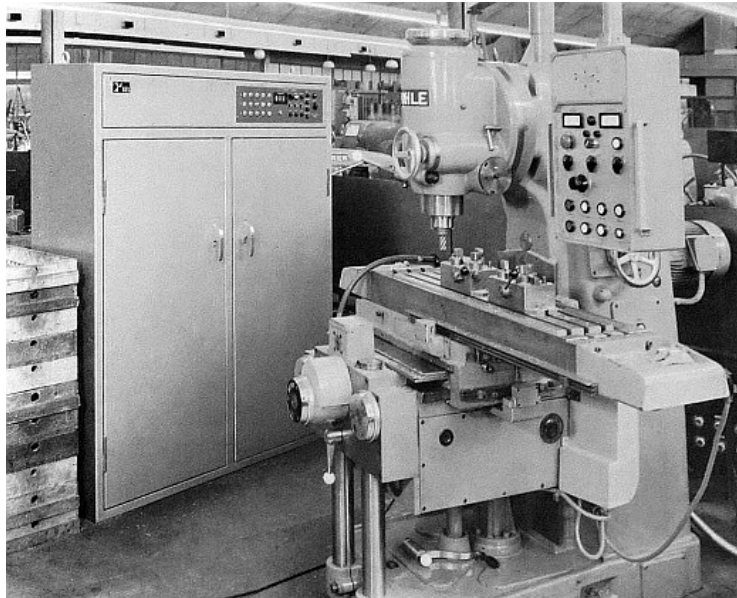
Bohle Fräsmaschine mit SEL-Steuerung⁸²³
